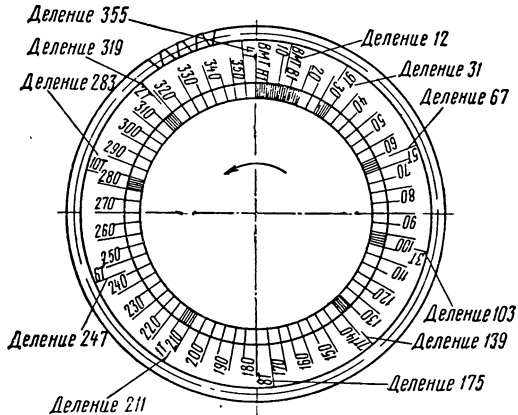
Схема разбивки на градусы ведущего диска пластинчатой муфты привода генератора и расположения на нем условных меток
